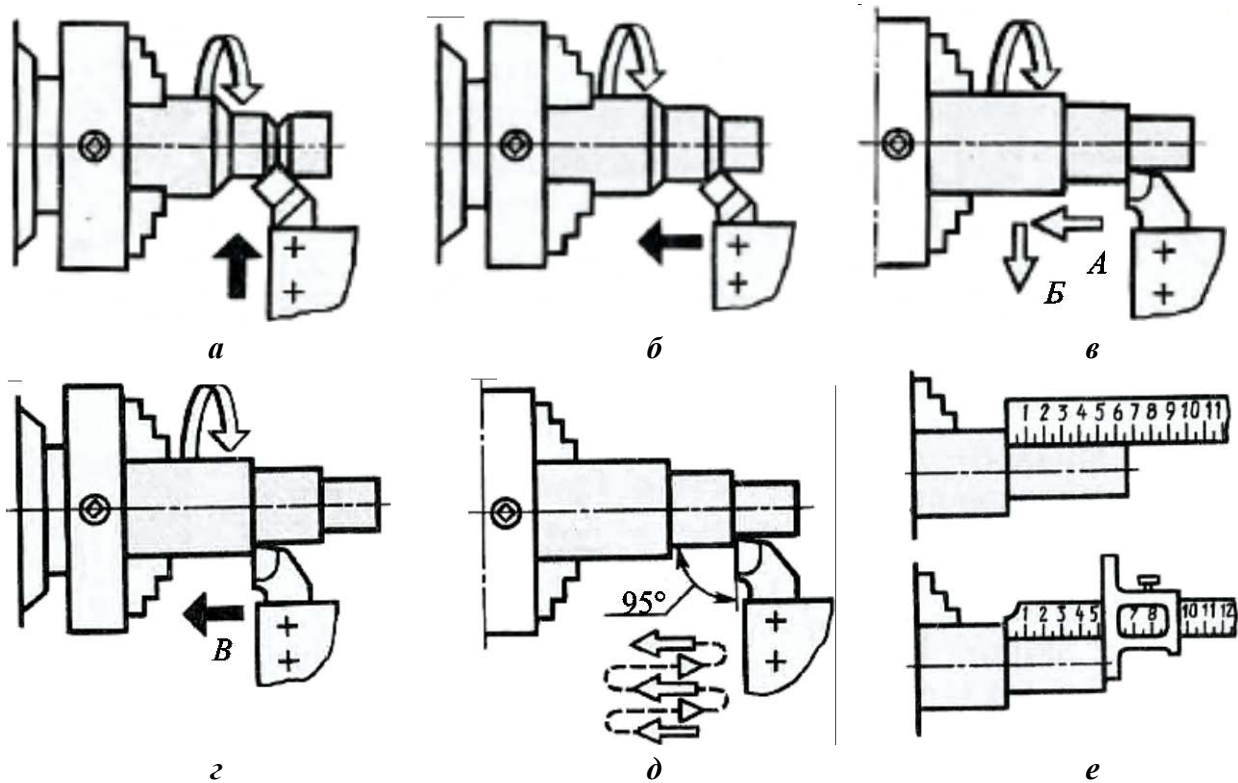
Прийоми обточування циліндричних поверхонь з уступами
